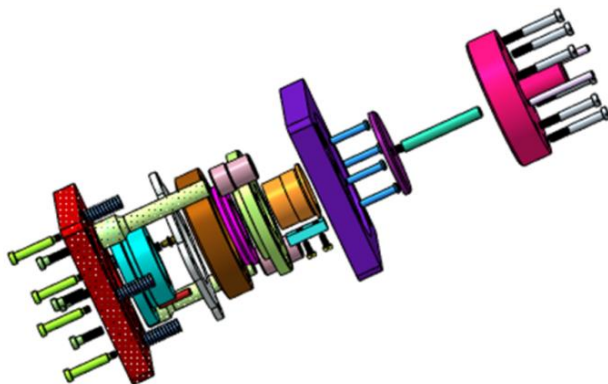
3D-модель «Штамп для изготовления пластин ротора»
